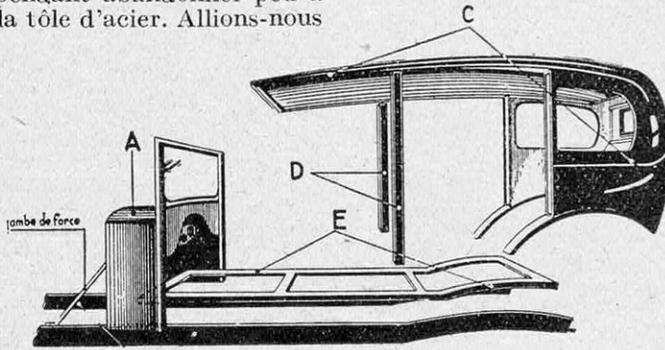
LA CARROSSERIE « SILENTBLOC » COMPREND QUATRE PARTIES PRINCIPALES (A, C, D, E) INDÉPENDANTES ET ASSEMBLÉES AU MOYEN DU « SILENTBLOC »
